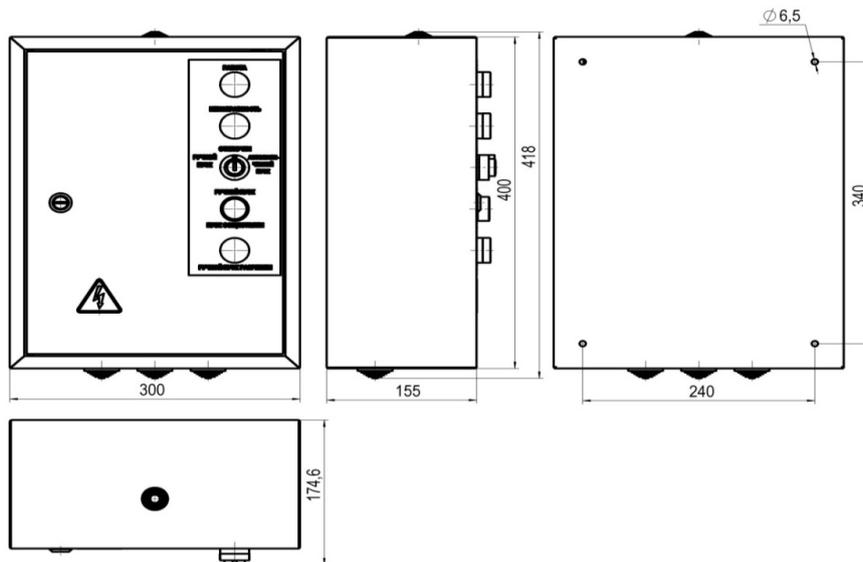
Габаритные и установочные размеры ШУП-3/ШУП-15.
